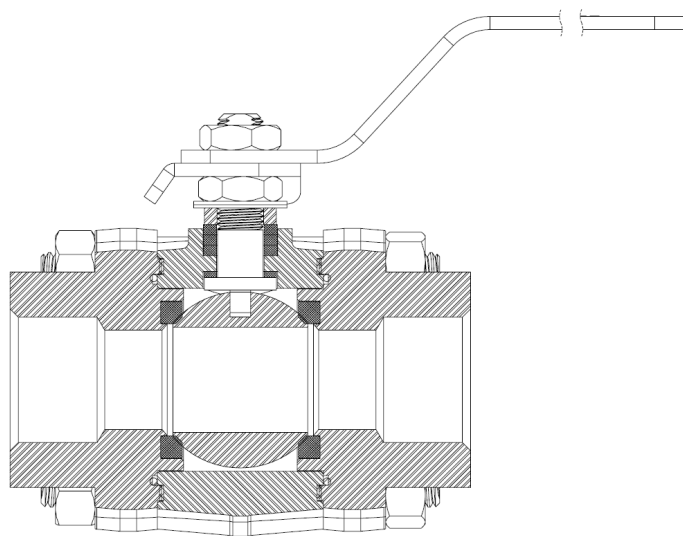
Corte transversal da VET Cl. 800 Montada.
